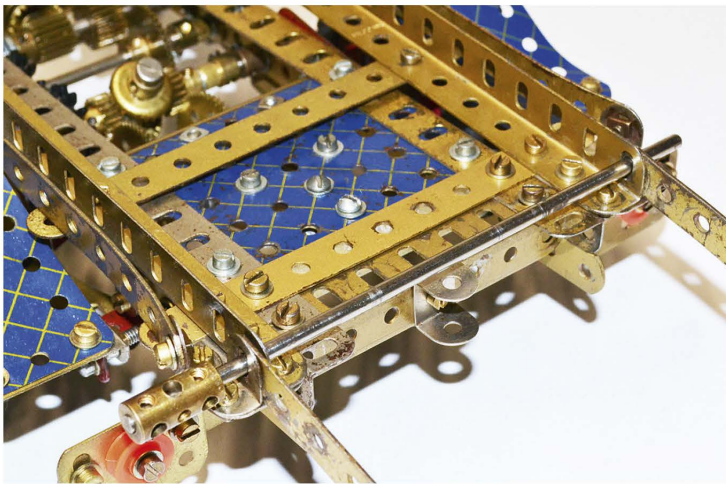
Gros plan sur la partie arrière du châssis montrant l'axe assurant la liaison de la rampe d'accès au plateau du camion pendant les opérations de chargement/déchargement
